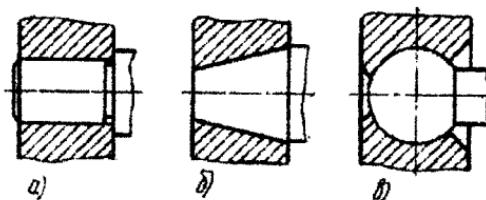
Основні типи цапф під підшипники ковзання.
